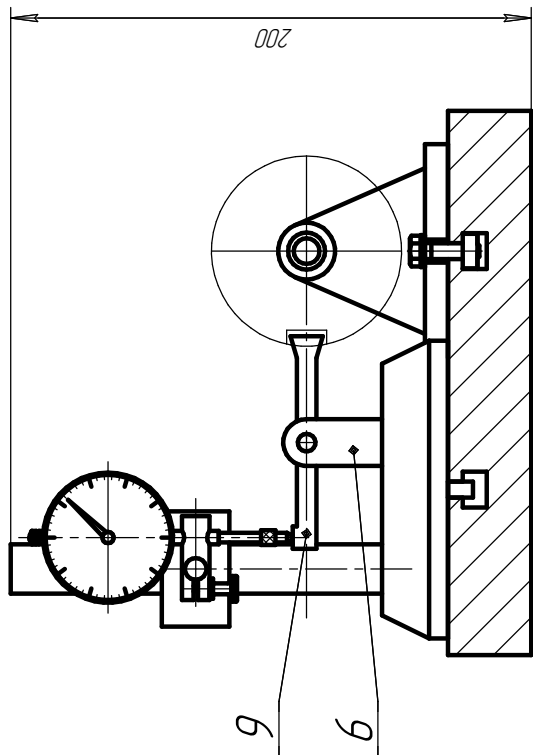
Схеми контролю циліндричних поверхонь деталей та їх базування
